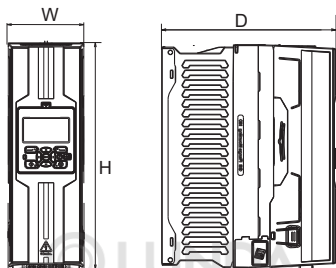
Габаритные размеры преобразователей частоты PRO-Drive-500 от 1.5 до 11кВт
